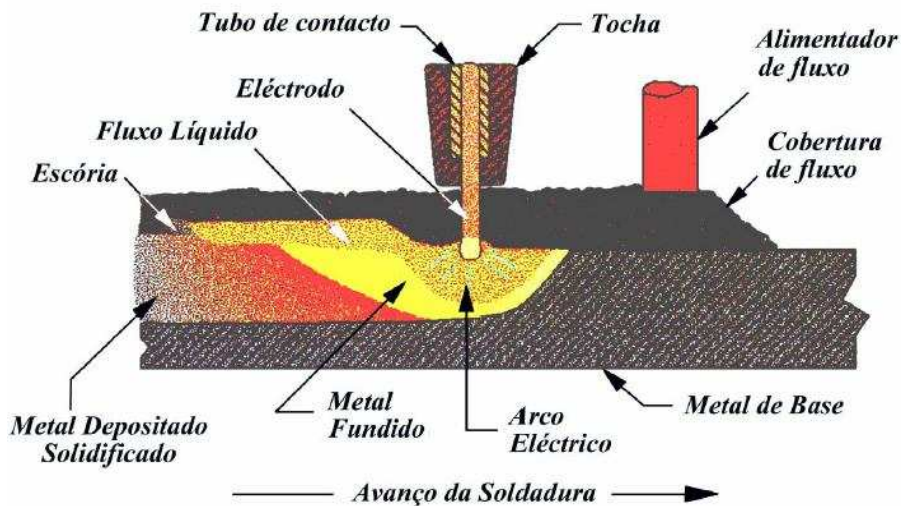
Representação do processo de soldadura por arco submerso³⁴
